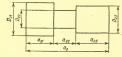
Эскиз цилиндрической заготовки со ступенчатым изменением диаметра
